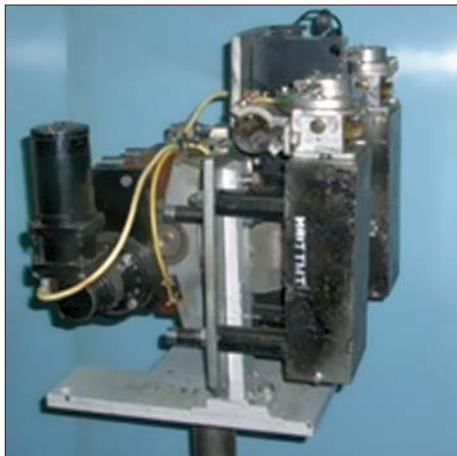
Оптико-механічний модуль для дистанційної підготовки поверхні та визначення залишкових напружень і твердості металу корпусів реактора ВВЕР-1000
